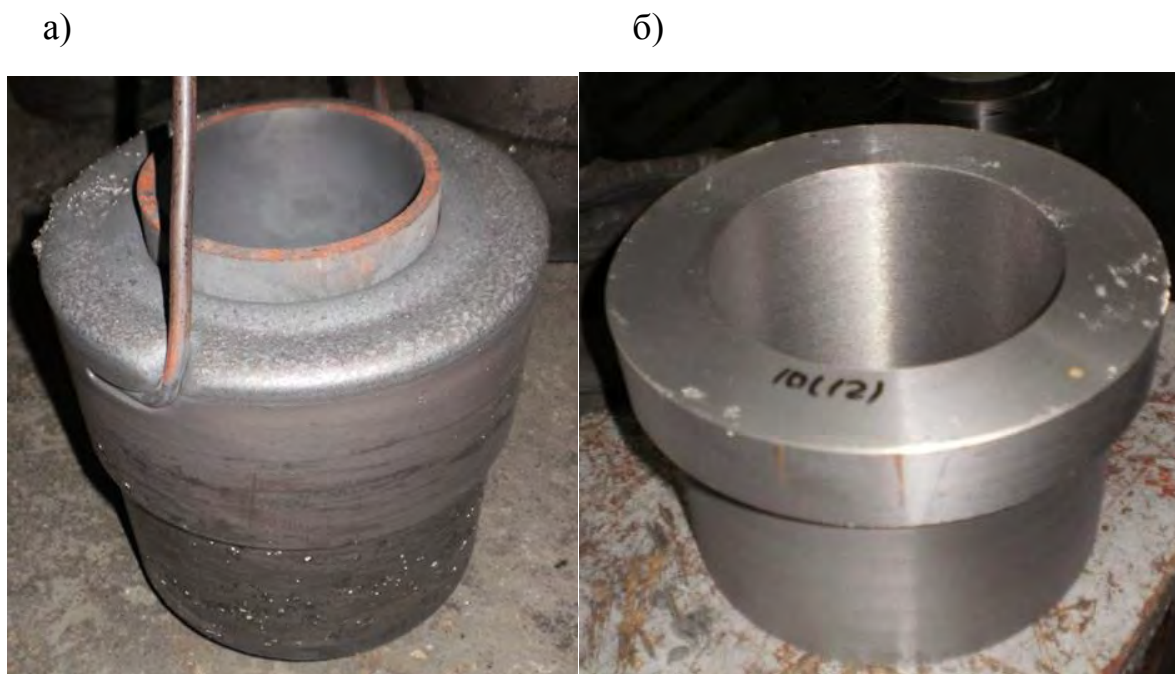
Отливка (а) из ВЧ для изготовления буртовой заготовки (б)
